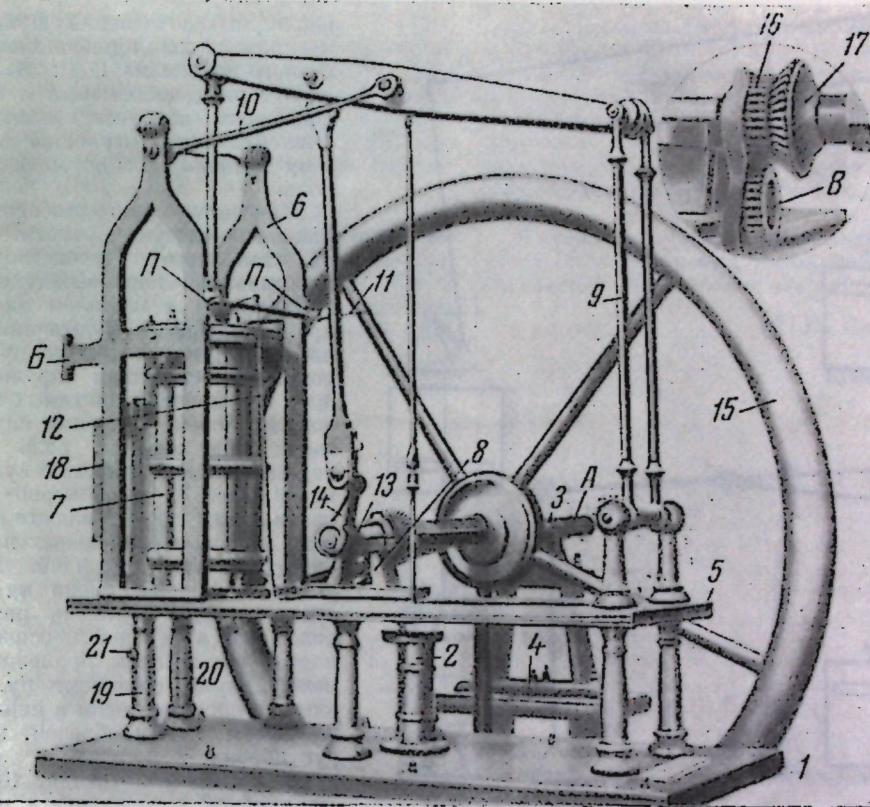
Внешний вид модели паровой машины М. Назукина:
